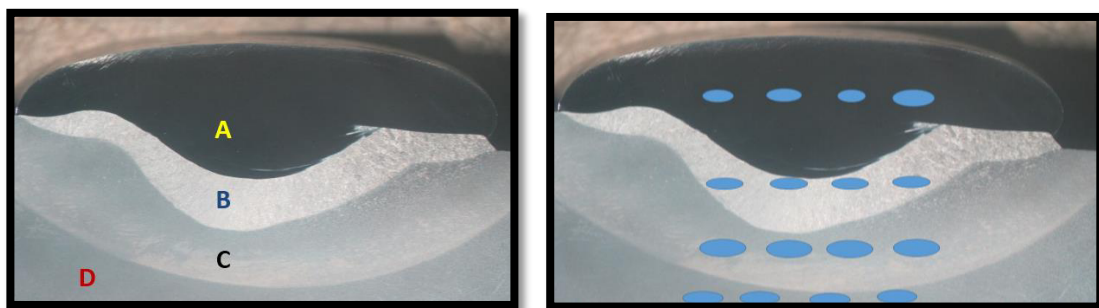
zonas para toma de durezas. A.-Soldadura de trabajo B.- Soldadura de aporte, C.-HAZ, D.-Material base.
